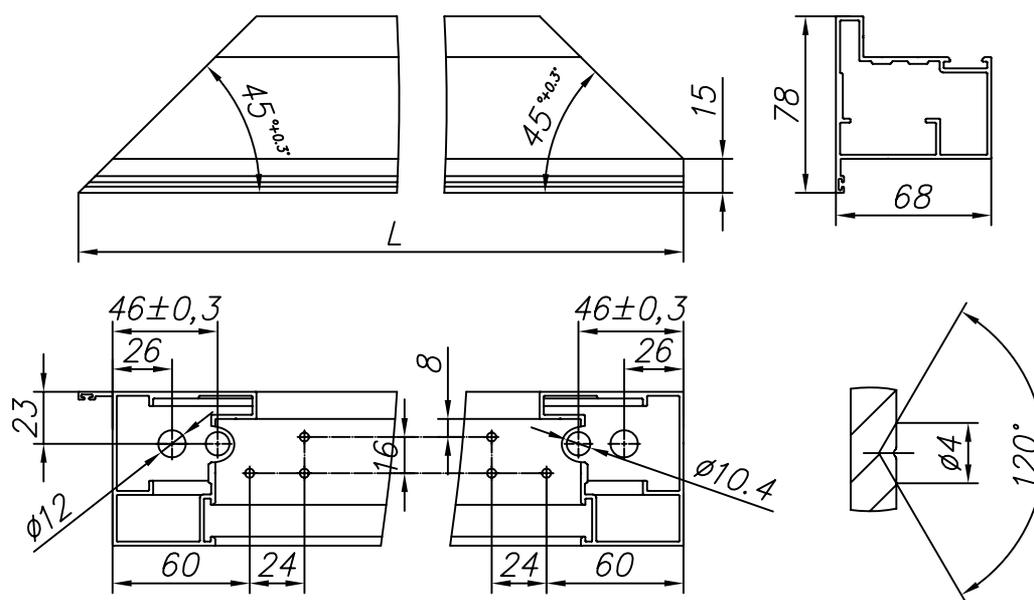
Изготовление стойки без паза для замка из профиля FLGU 400.0108
